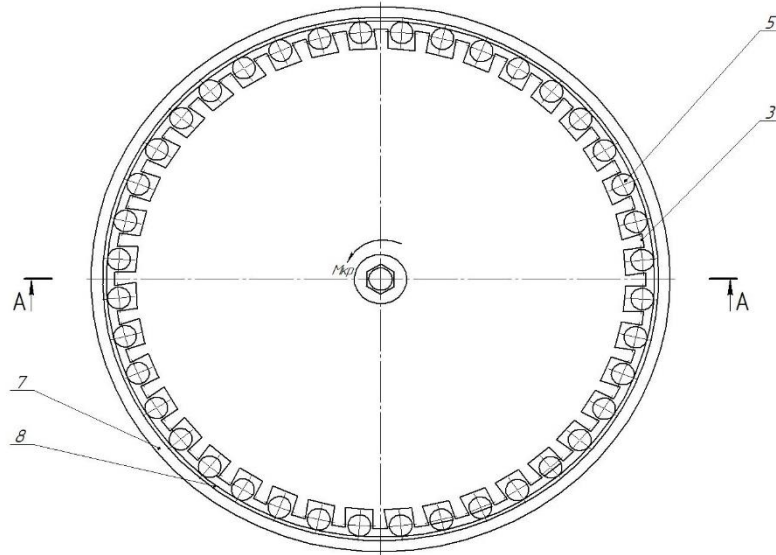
Устройство для шлифовки сферических тел (вид сверху)
